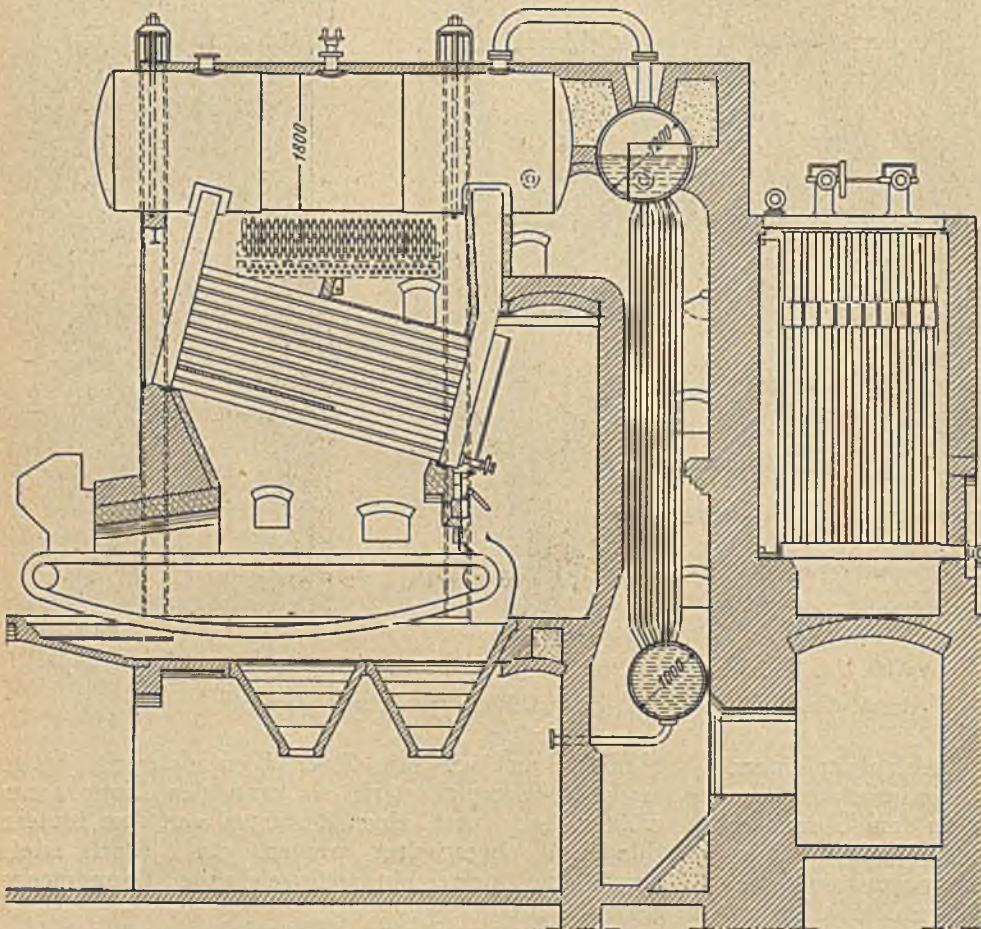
Längsschnitt durch den Universalkessel von Steinmüller.
